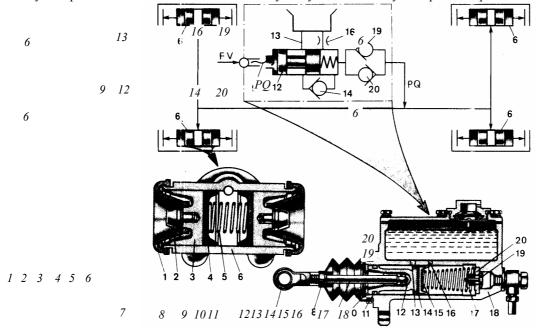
Одноконтурный гидростатический тормозной привод: 1 — защитный колпак; 2, 9 — толкатели; 3, 12 — поршни; 4, 11, 15 — манжеты; 5, 17 — пружины; 6 — корпус рабочего цилиндра; 7 — серьга; 8 — контргайка; 10 — упорная шайба; 13 — перепускное отверстие; 14 — обратный пластинчатый клапан; 16 — компенсационное отверстие; 18 — корпус главного цилиндра; 19 — выпускной клапан; 20 — впускной клапан
